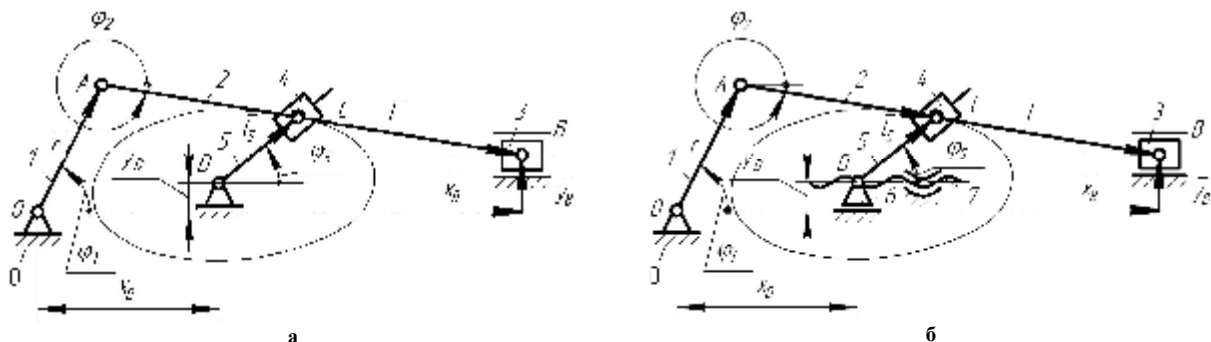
Двокривошипний шарнірний чотириланковий механізм: а) $a = \text{const}$; б) $a \neq \text{const}$
